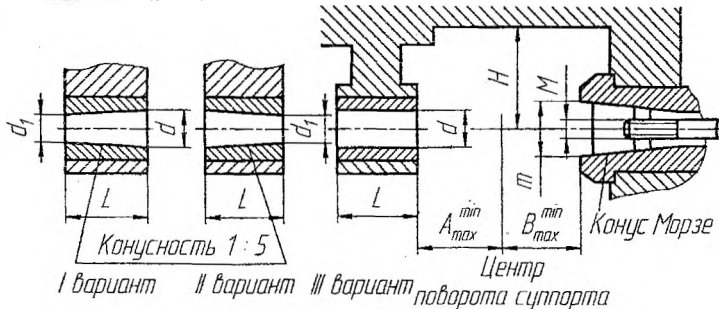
Размеры заднего подшипника и конца шпинделя суппорты зубофрезерных станков
